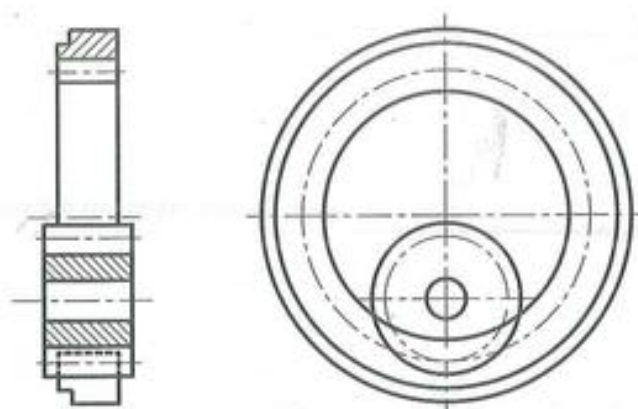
Engranaje interior de ruedas cilíndricas.
